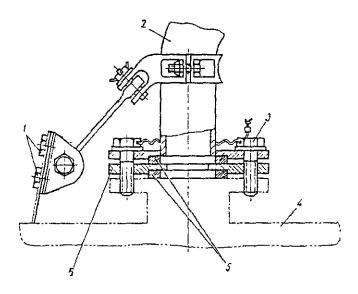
Установка патрубка отбора воздуха на ПОС: t, 3 - болты; 2 - патрубок отбора воздуха на ПОС; 4 - твигатель АИ-24, 5 - медная прокладка; 6 - дроссельчая шайба
